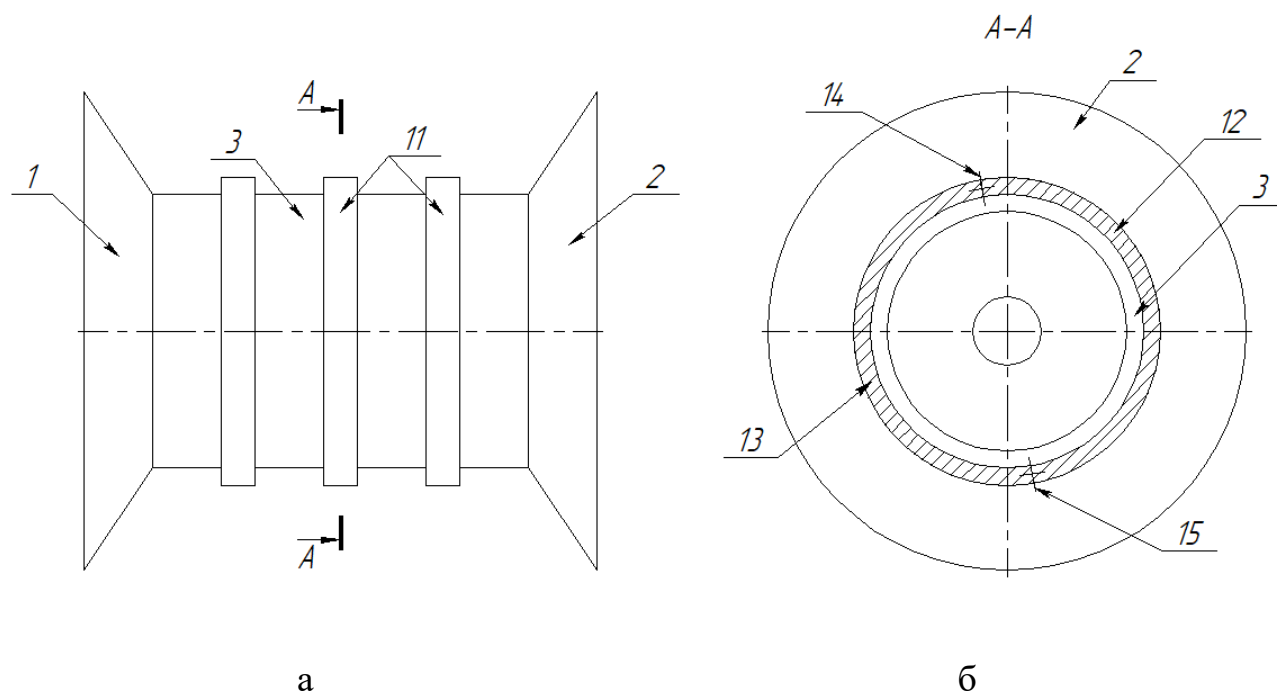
а. Каток опорный картофелеуборочного комбайна ККР-2 (модернизированный) вид спереди; б - разрез А-А катка опорного [78]
